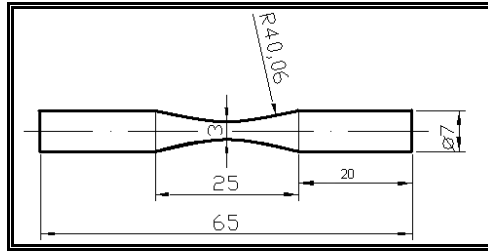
Цилиндрический образец для усталостных испытаний по схеме «изгиб с вращением»
